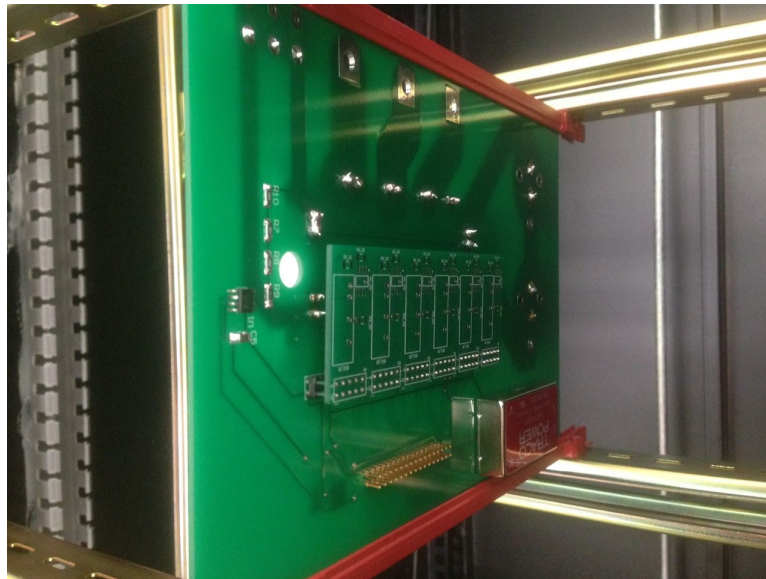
Vista lateral derecha de montaje de celda en soporte construido sin disipador
